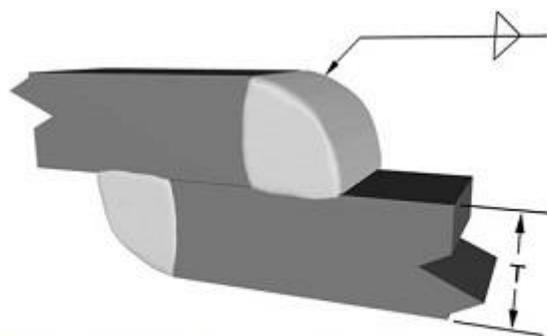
Unión por soldadura de tipo 3.
